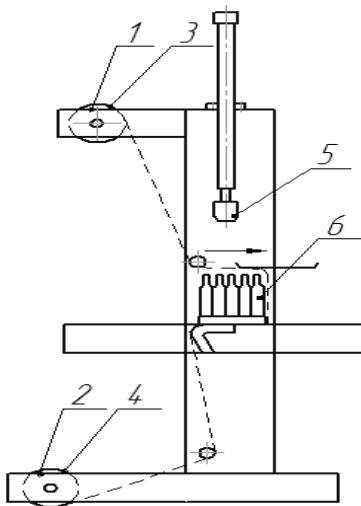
Схема механізму утворення рукава пакувального матеріалу.
